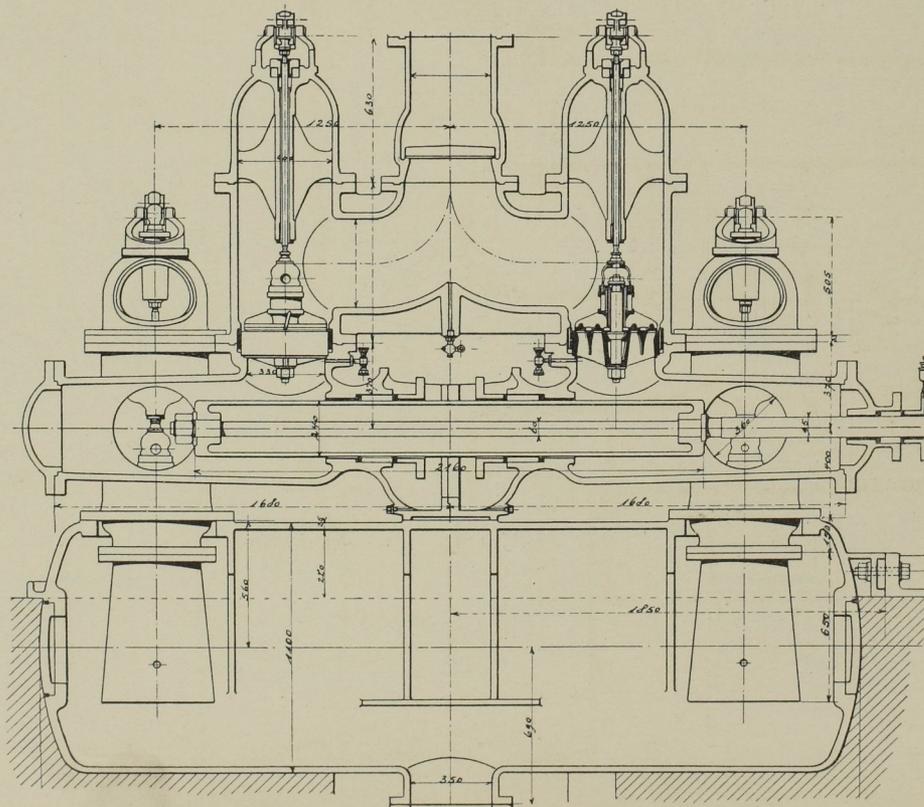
Längsschnitt durch die Druckpumpe. Masst. 1:30.
